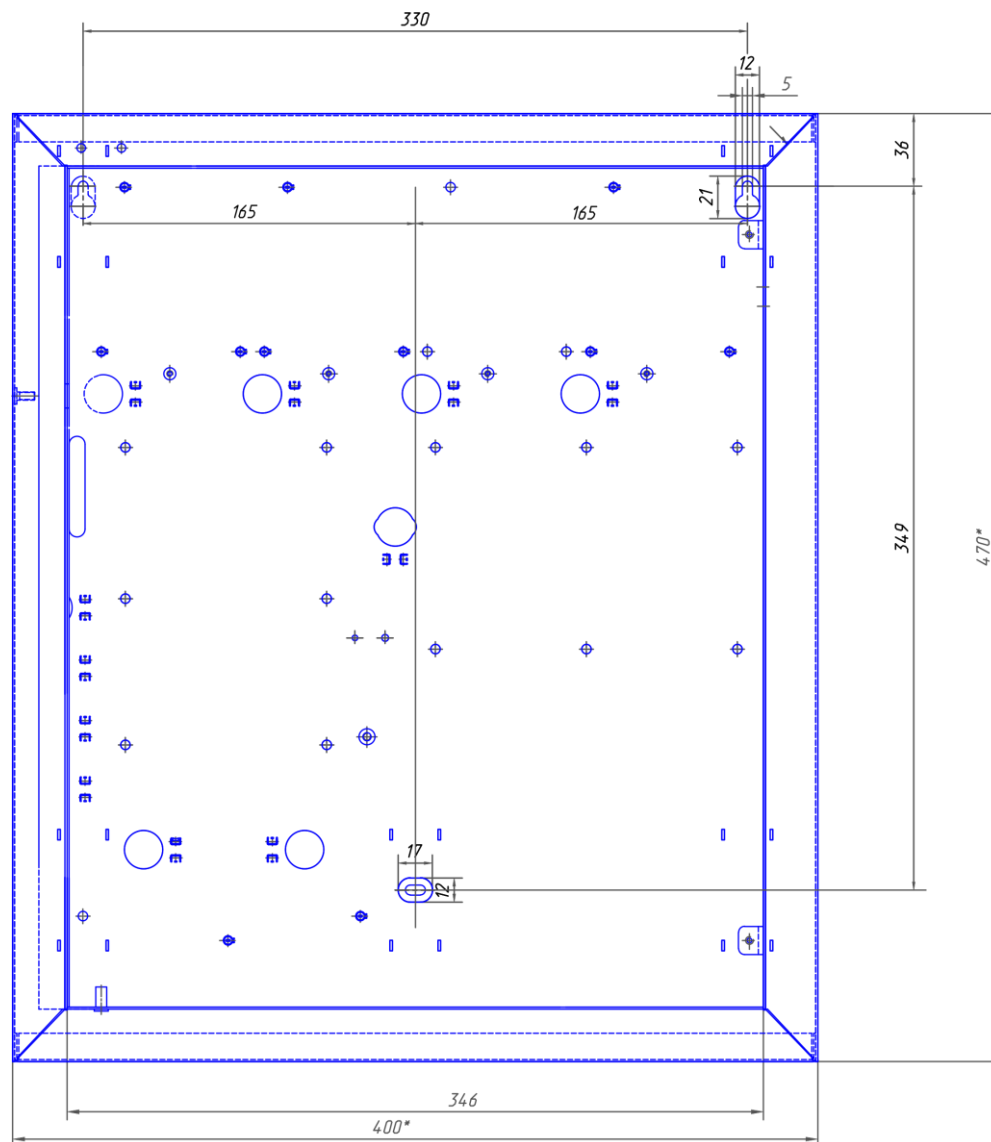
Установочный чертеж АПКП.ХР777 и АПКП.ХРА6
